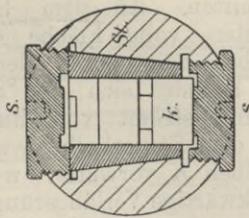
a, Querschnitt durch den Kolbenschieber.
